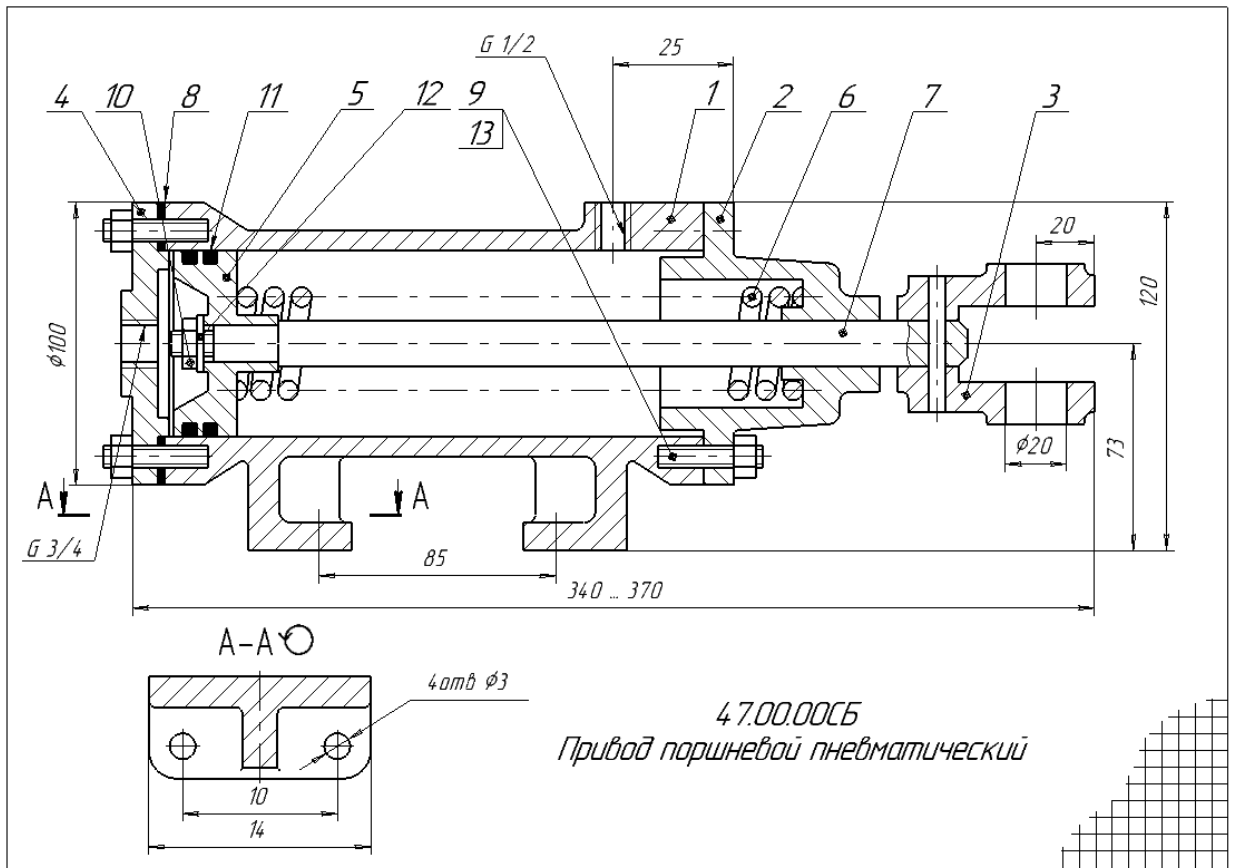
Образец выполнения задания ИГ 9.3 Сборочный чертеж
